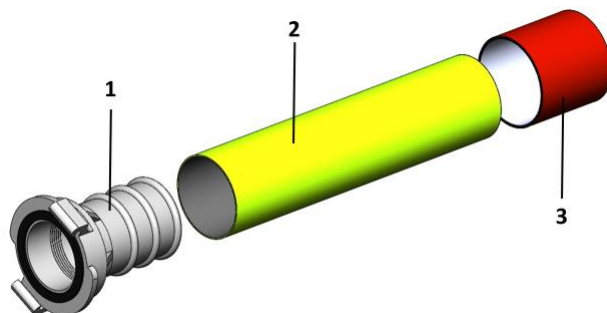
Трехмерная модель предлагаемого решения: 1 – соединительная головка, 2 – пожарный рукав, 3 – конусная втулка
